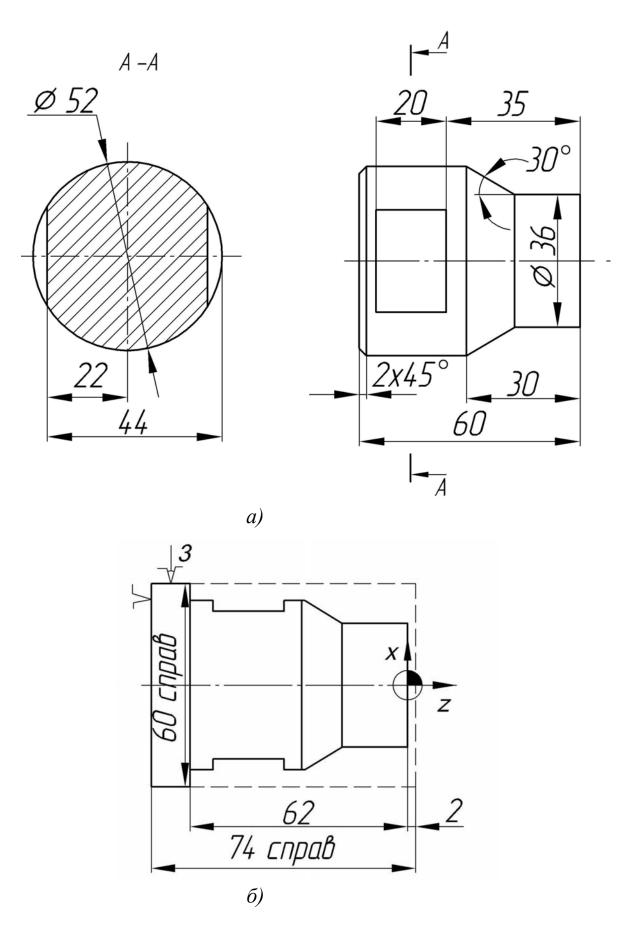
Токарно-фрезерная обработка детали на многофункциональном станке: a — чертеж детали; δ — эскиз выполнения детали на установе A
